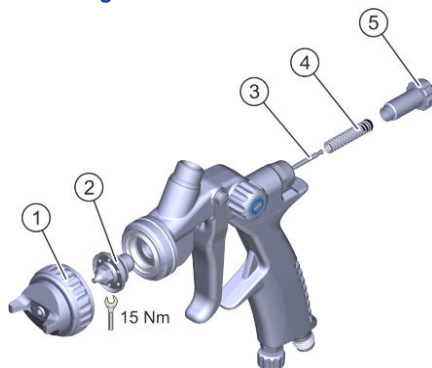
Démontage de l'aiguille et de la buse (version standard)
